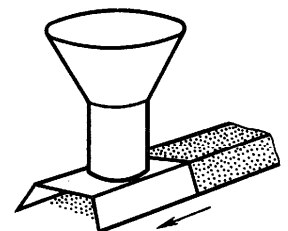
Дозатор флюса при сварке по флюсу
